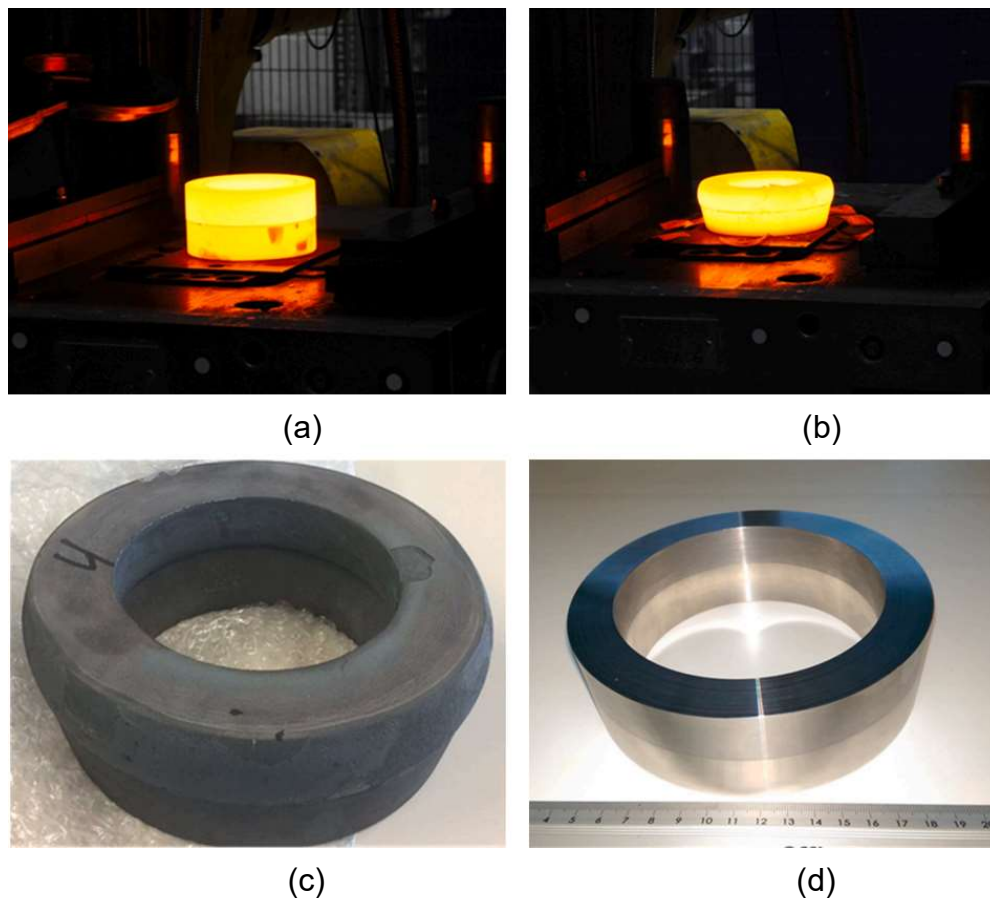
(a) Pré-forma bimetalica aquecidas antes do forjamento, (b) após o forjamento, (c) anel soldado por forjamento após resfriamento a ar, (d) peça final usinada [23].
